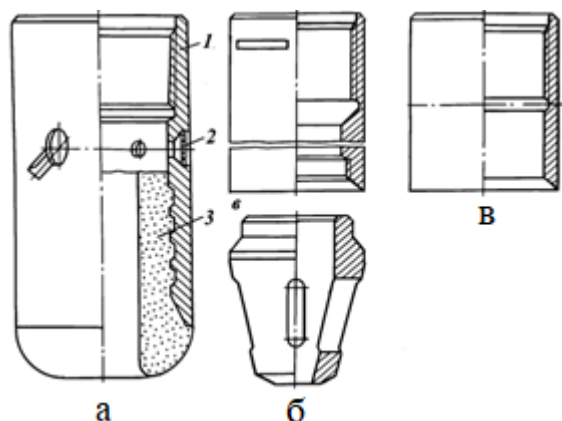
Башмаки колонные: а – типа БКМ: 1 – корпус; 2 – заглушка; 3 – направляющая насадка; б – типа БП с чугунной направляющей насадкой; в – направляющая насадка; г – типа Б
